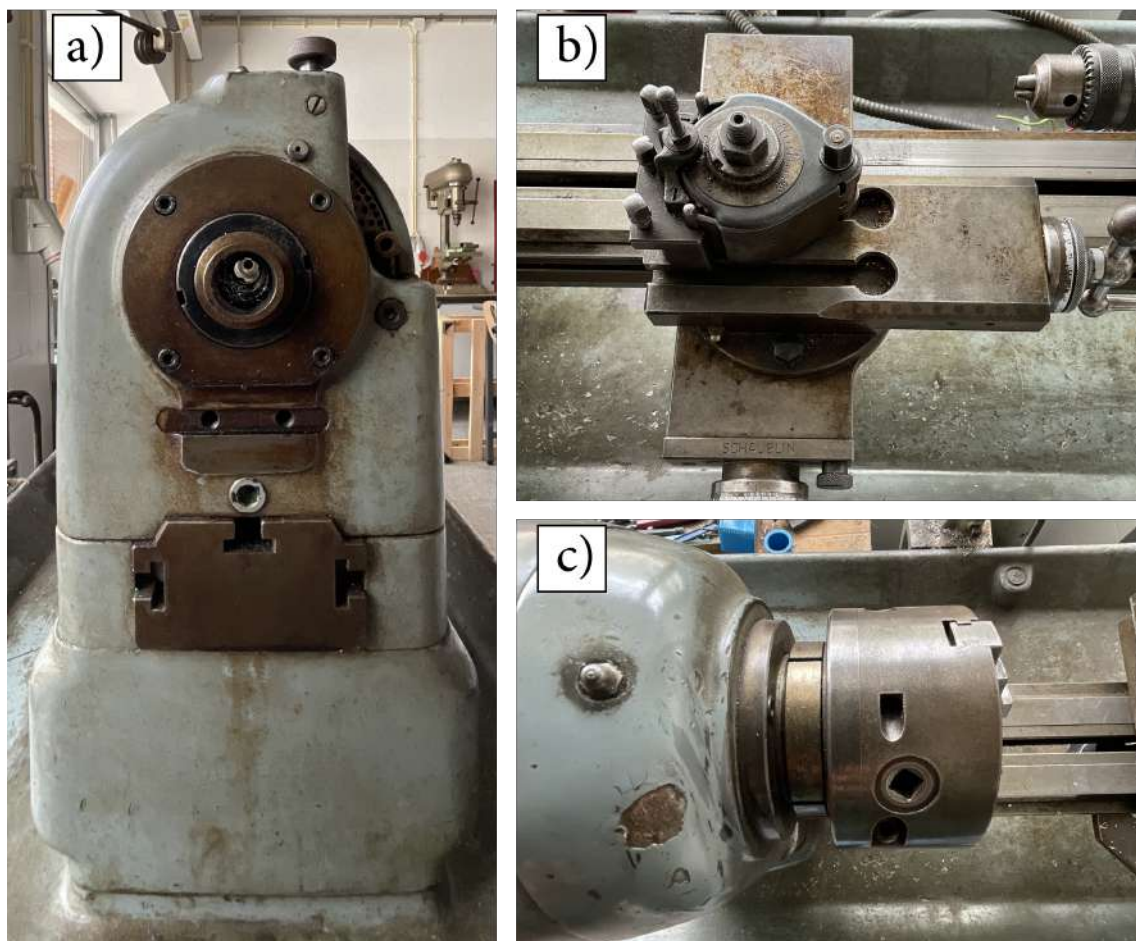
Corrosão e deterioração dos equipamentos: a) Torno (vista lateral esquerda); b) Carro (vista superior); c) Bucha e cabeçote fixo (vista superior).
